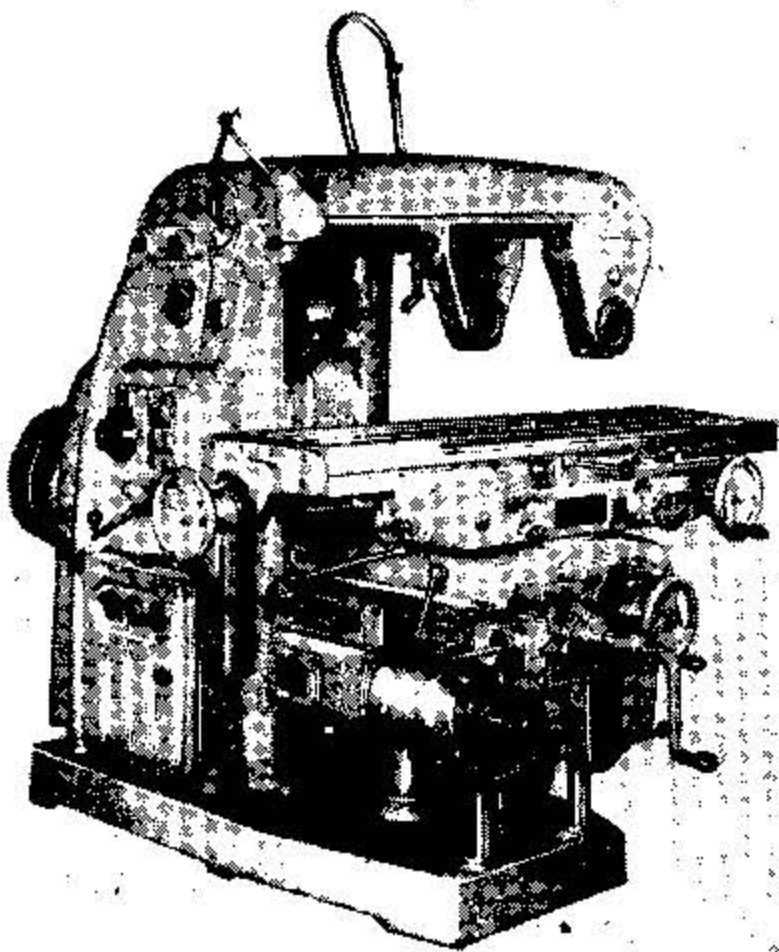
Универсальный консольно-фрезерный станок модели 6М83
